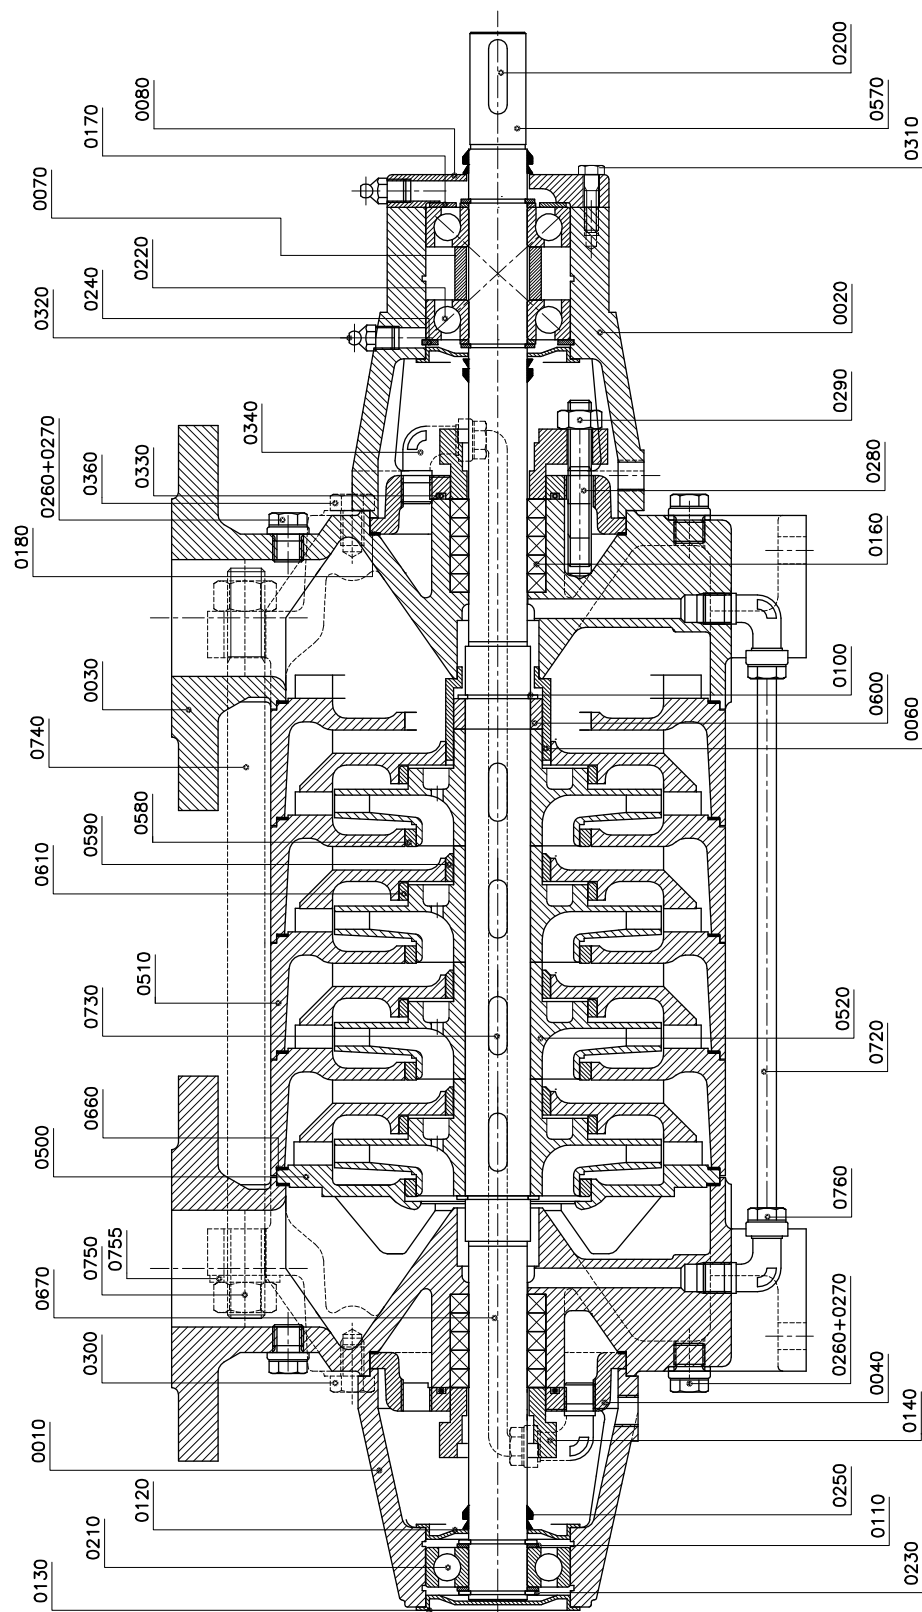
MCH 14a/b med tung lagerkonstruksjon.
